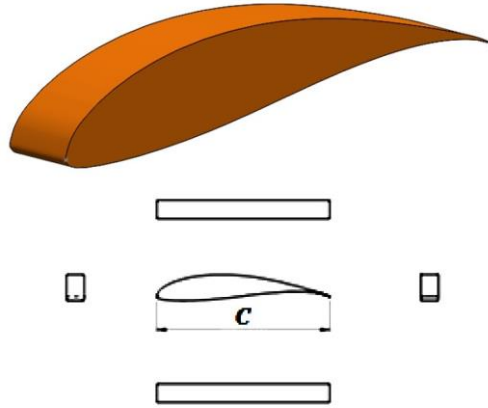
Profil Wortmann 'FX 63-137' et sa mise en plan
